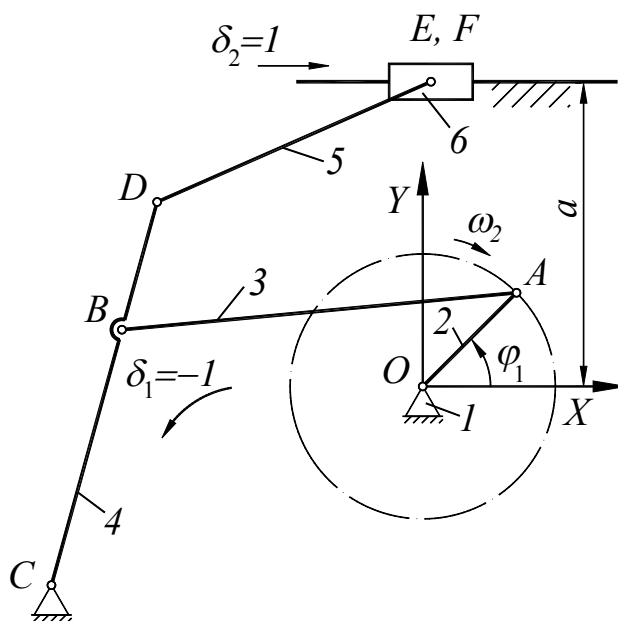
Кинематическая схема механизма подачи заготовок
